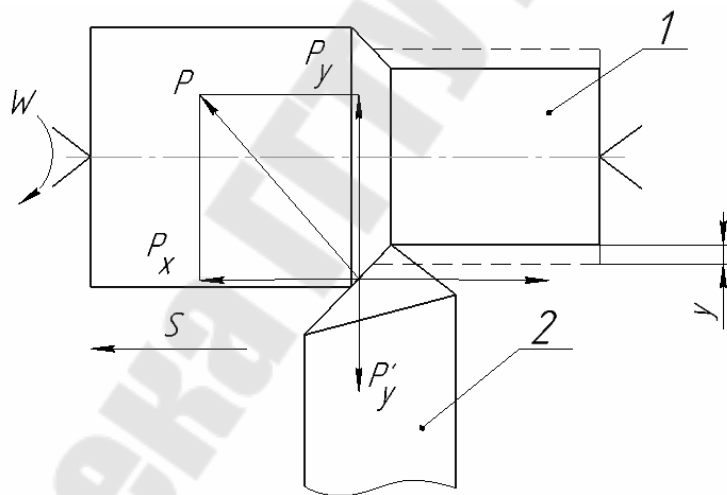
Схема обработки заготовки на токарном станке:
